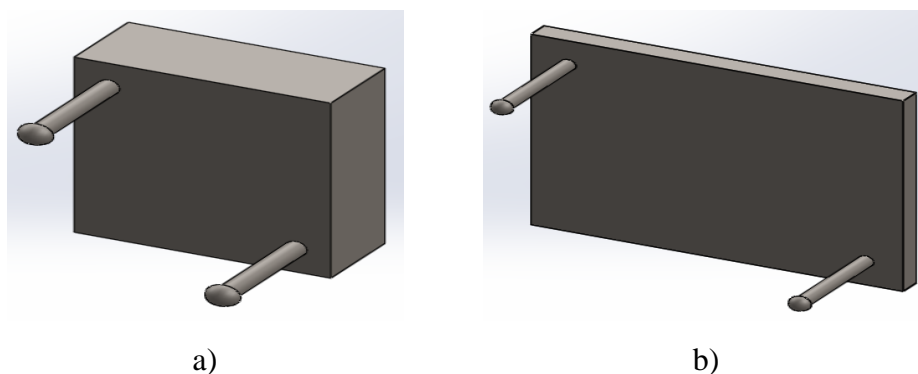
a) Compactador del molde de compresión y Dureza, b) compactador del molde de tracción
